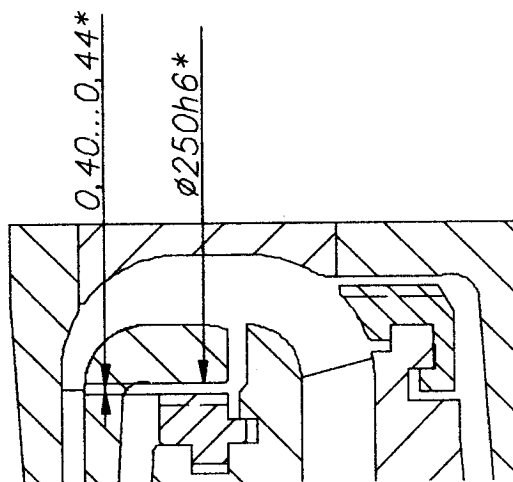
Фрагмент проточної частини відцентрового компресора
